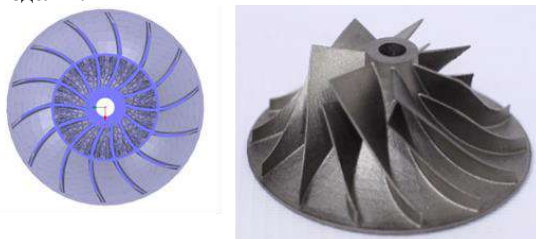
3D модель колеса компрессора и фото изготовленного колеса компрессора на 3D принтере компании ООО «ЛарТехнологии».
